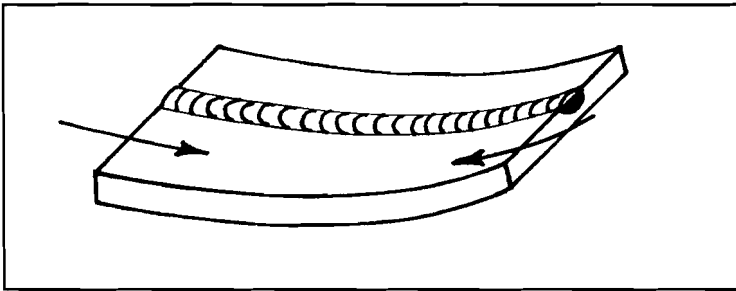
DEFORMACIÓN POR CONTRACCIÓN LONGITUDINAL
